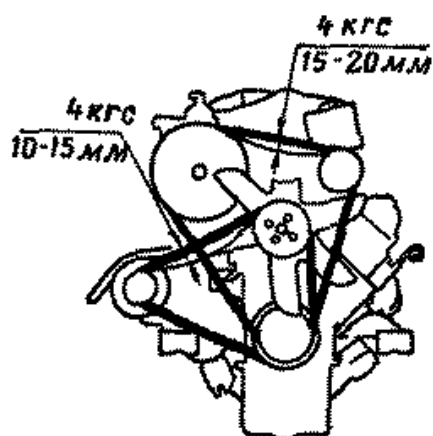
Схемы проверки натяжения ремней привода компрессора (насоса гидроусилителя руля) и ремня привода генератора и вентилятора
